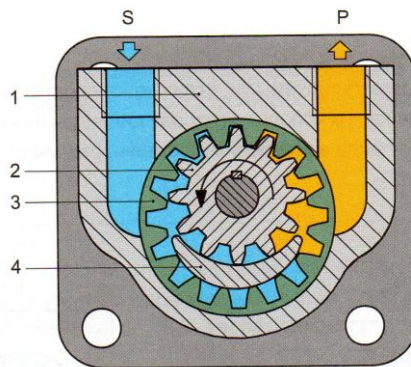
, в. Схема шестеренного насоса с внутренним зацеплением: 1 – корпус насоса; 2 – внутренняя шестерня; 3 – внешняя шестерня; 4 – серповидный сегмент (конструктивный элемент, разделяющий всасывающую и нагнетательную полости)..
